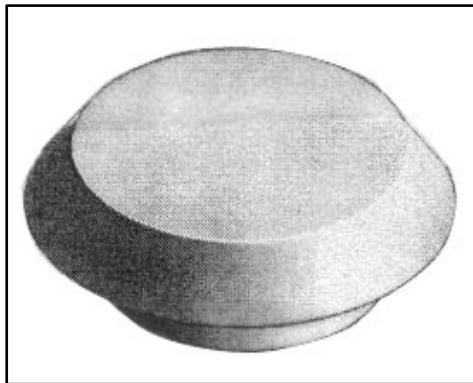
PLAN INCLINÉ EXTÉRIEUR
